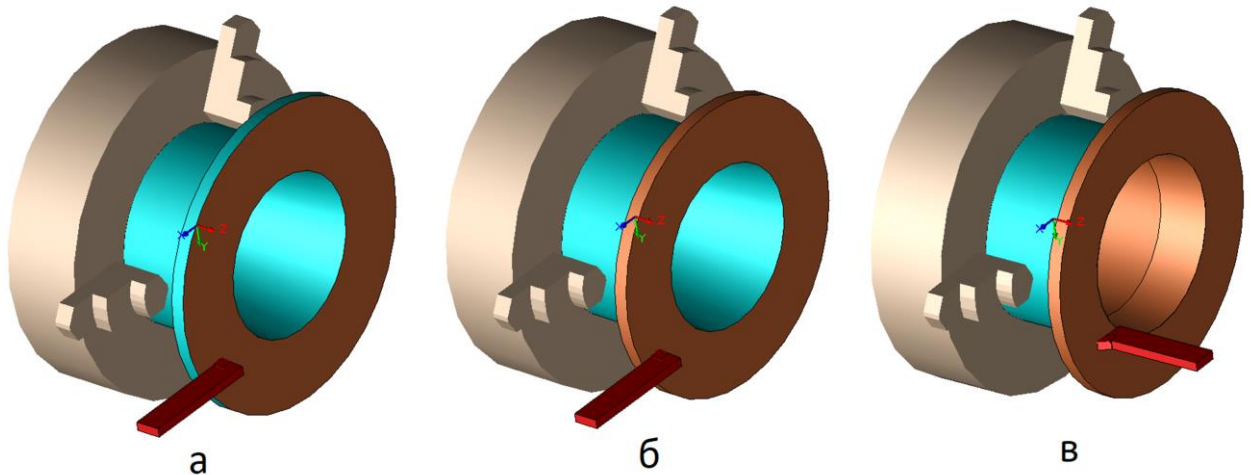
Фрагменти імітації процесу обробки деталі: а – підрізання торця; б – чорнове точіння; в – чорнове розточування;
